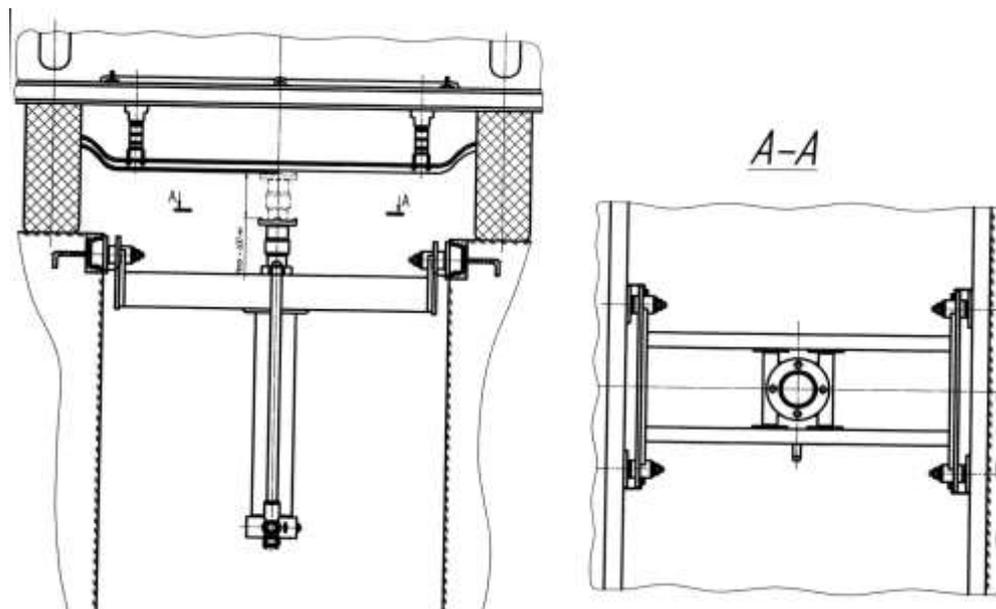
Общий вид разрабатываемого подъемника для агрегатов.
